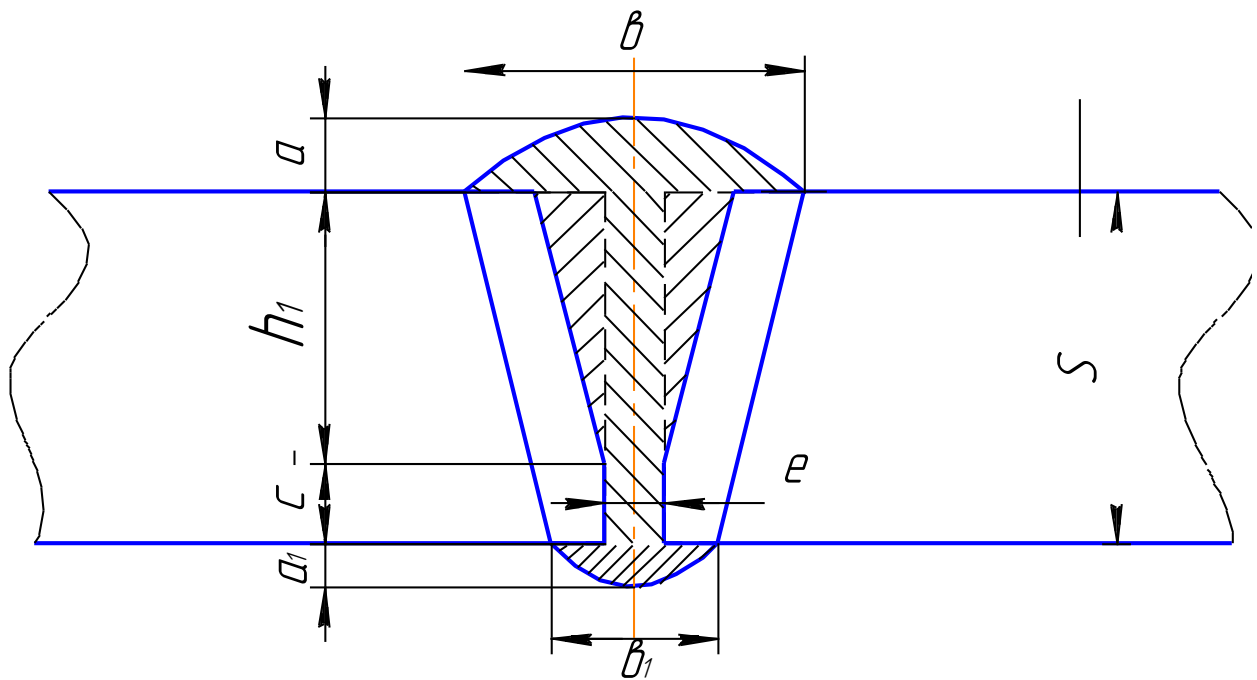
Конструктивні елементи підготовки кромки і зварного шва:
